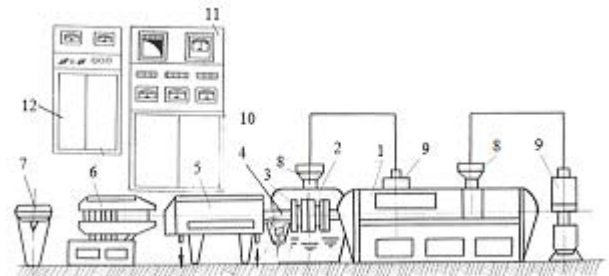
Опытно-промышленный экструзионный агрегат для изготовления многослойных полимерных труб с применением ультразвука: 1 – экструдер АТЛ-45-П; 2 – экструдер ЧП-40; 3 – экструзионная головка; 4 – калибрующая насадка; 5 – охлаждающая ванна; 6 – тянущее устройство; 7 – отрезное устройство; 8 – бункер с устройством для подсушки и подогрева гранул; 9 – пневмозагрузчик; 10 – электрощит; 11 – магнитострикционный преобразователь ПСМ6-22; 12 – ультразвуковой генератор УЗГ1-4
